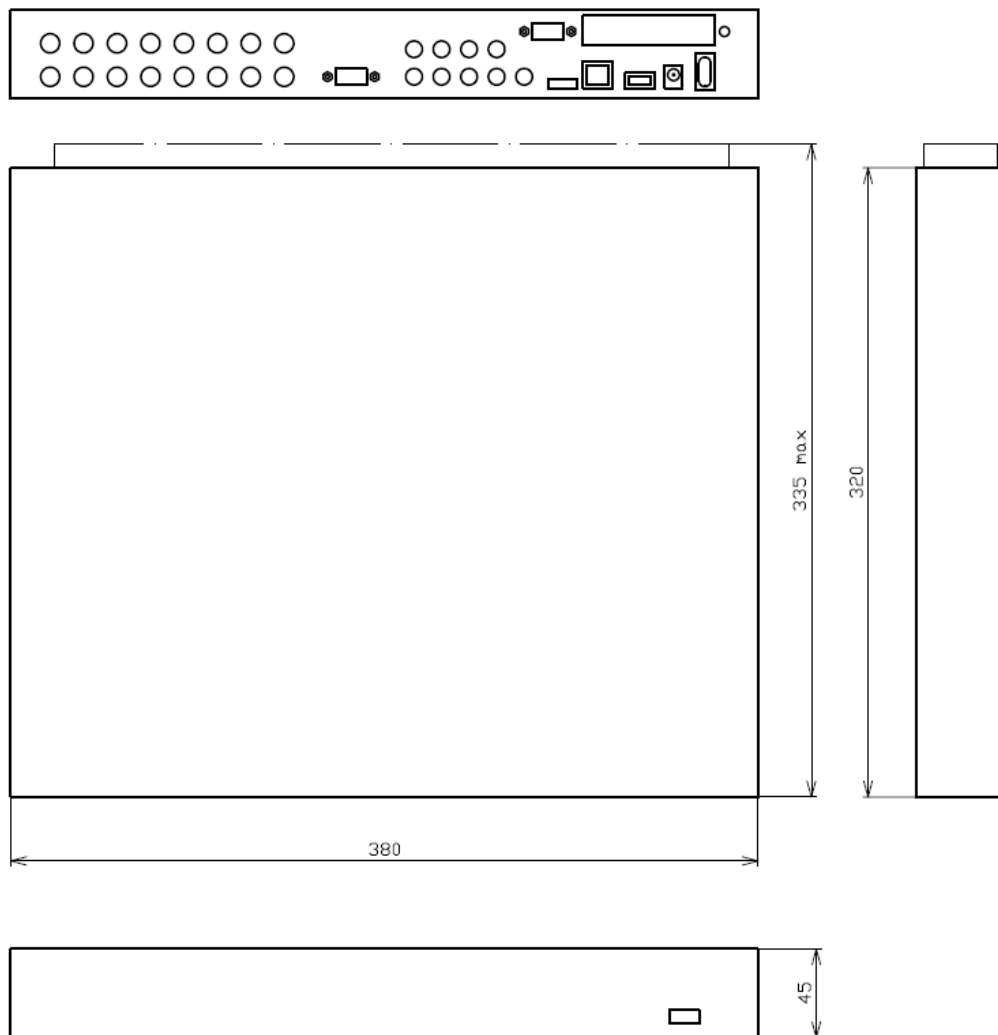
Габаритный чертеж ИВМ-8016.
